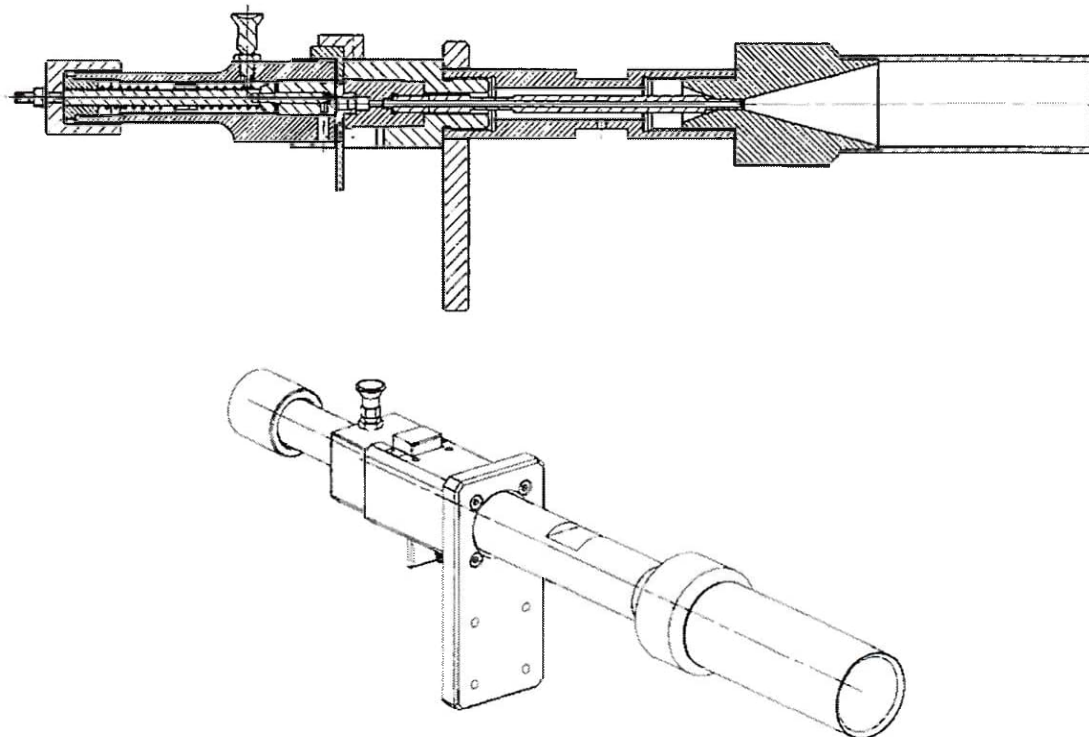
Exemple de banc d'essai alternatif (vue latérale et coupe longitudinale)
